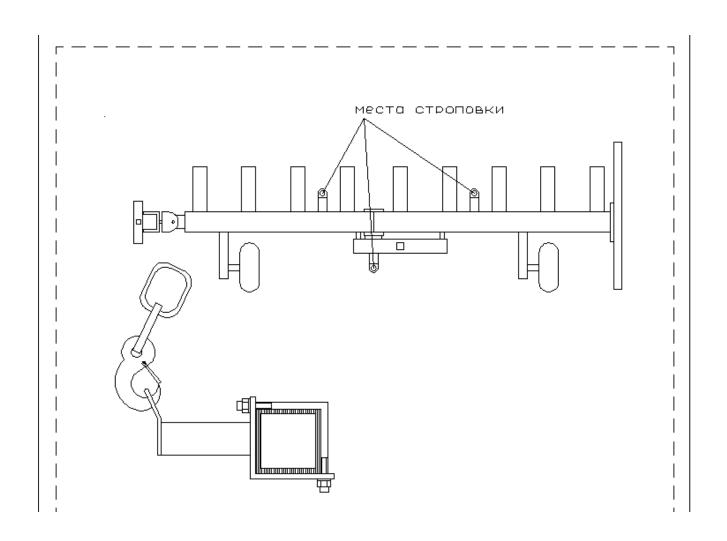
Схема строповки культиватора КМН-5,6/5,4.
